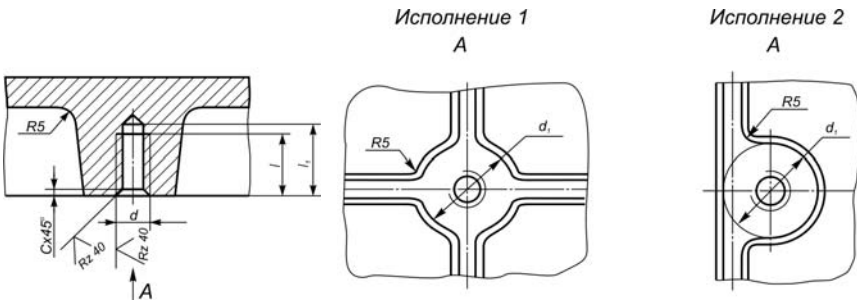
Приливы для крепления стержневых ящиков к промежуточной плите
